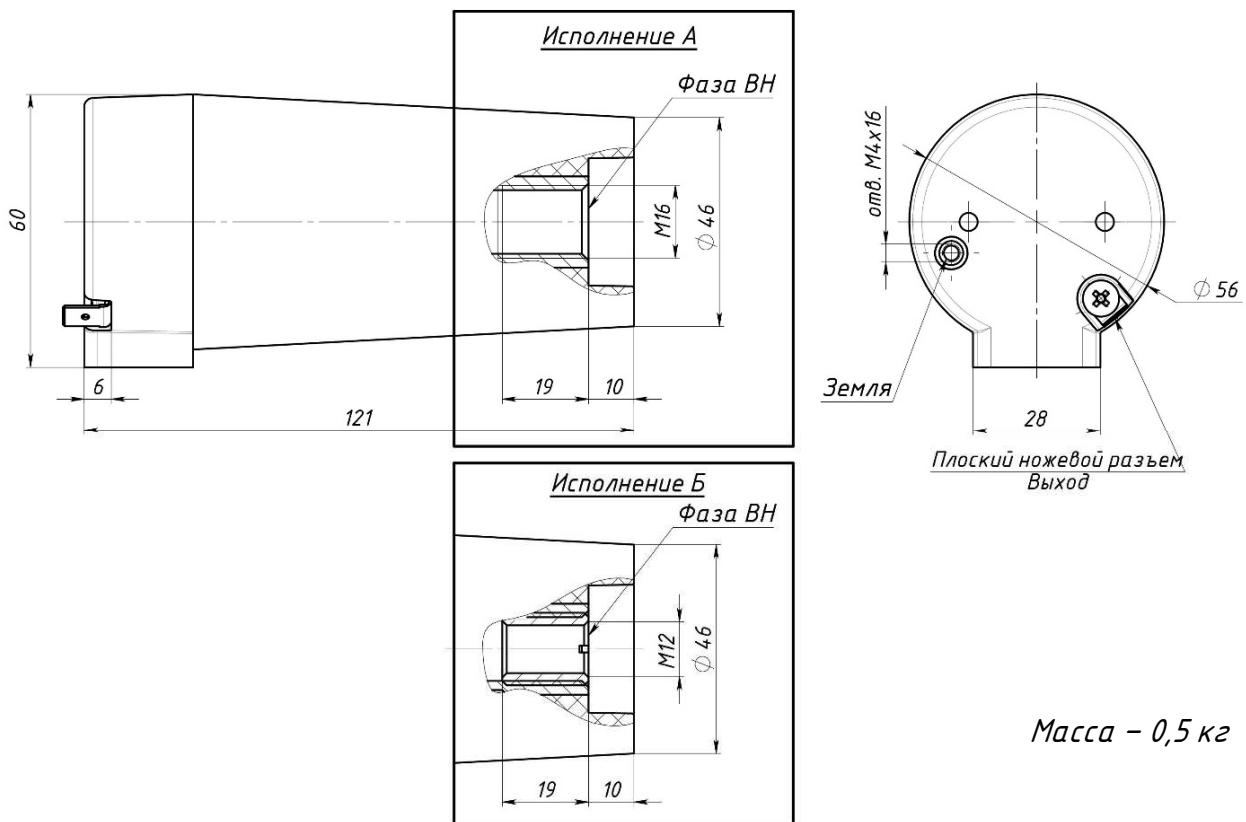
Габаритные и присоединительные размеры РЭС
